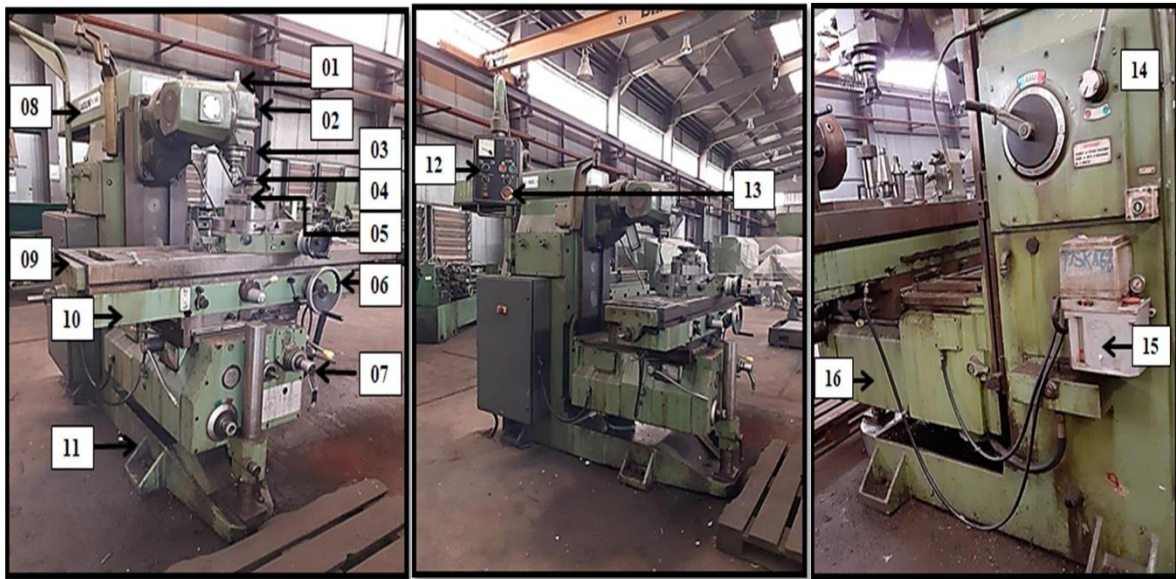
les composants de la fraiseuse FU-1800 [60].
